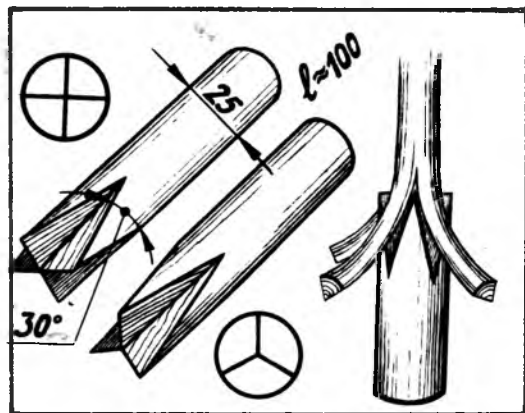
Щепало: а — с тремя резцами; б — с четырьмя «резцами»
